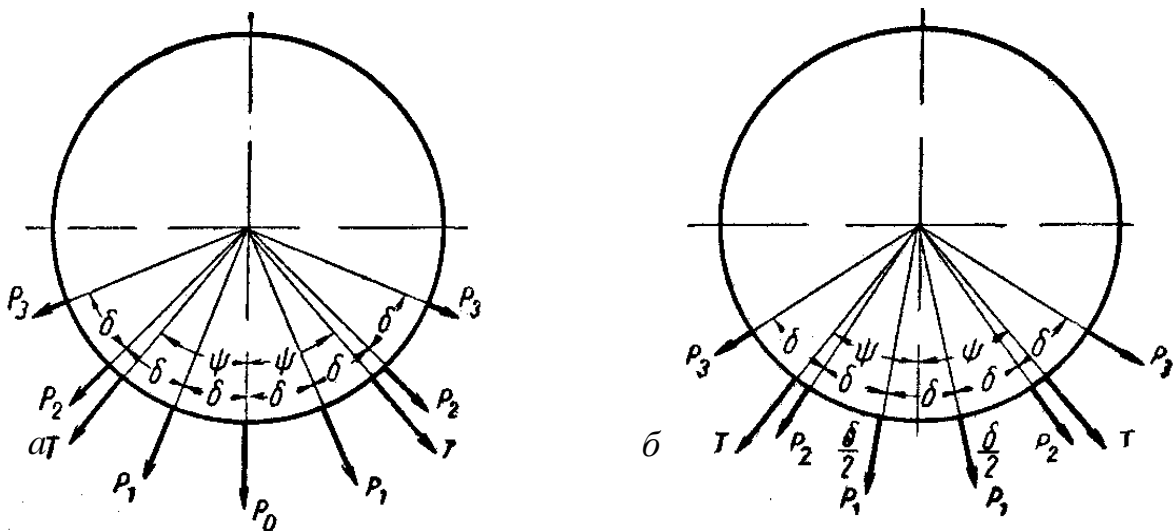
Схема нагрузок на бандаж, опирающийся на несколько башмаков:
